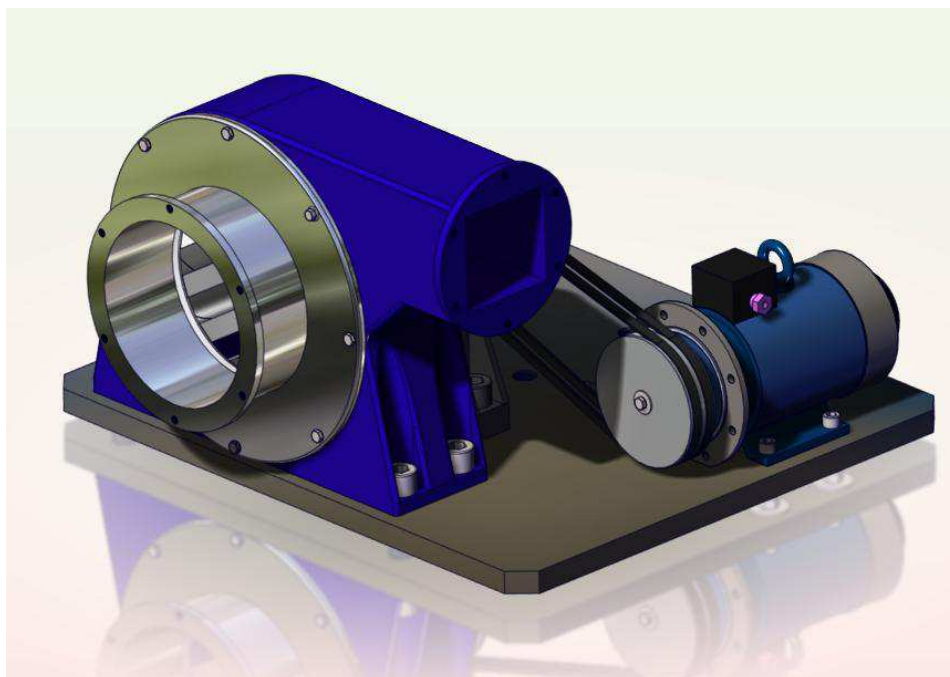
3D модель зборки вентилятора (вид 1).
